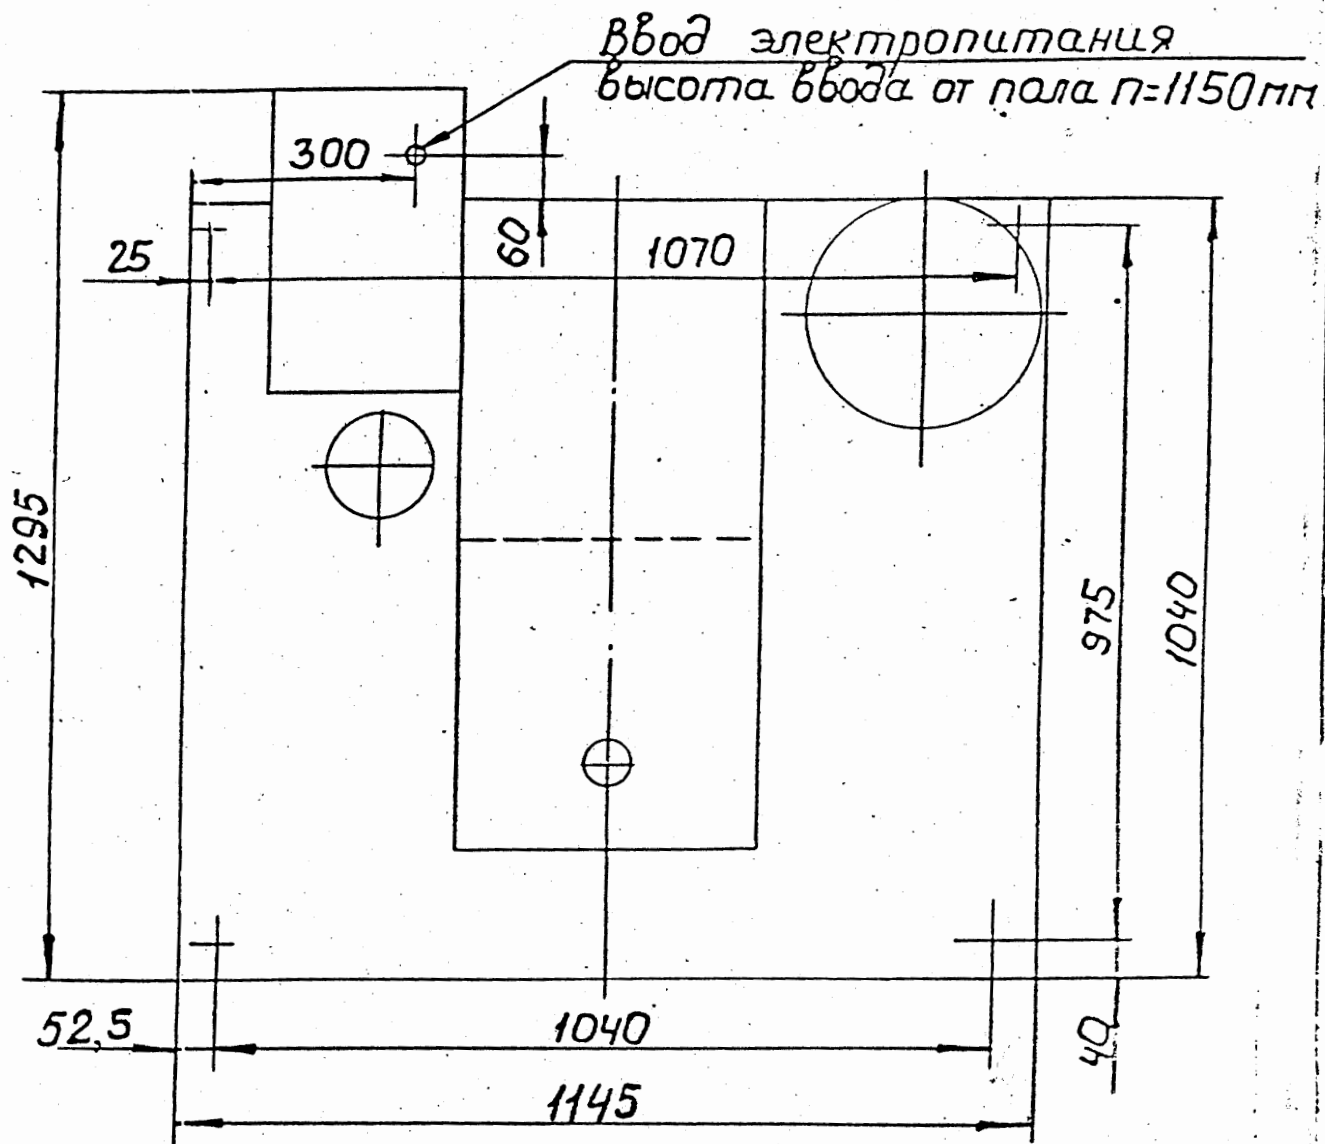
Установка станка исполнителя ОУ без приставного оборудования
